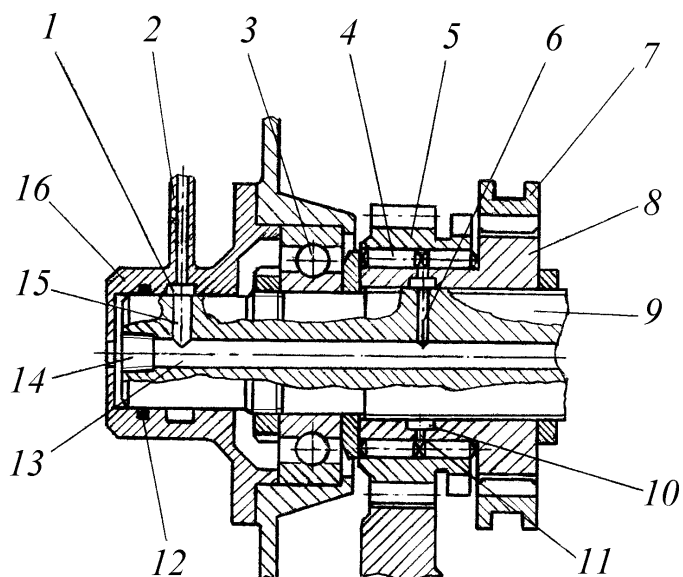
Смазывание игольчатых подшипников шестерни в КП
